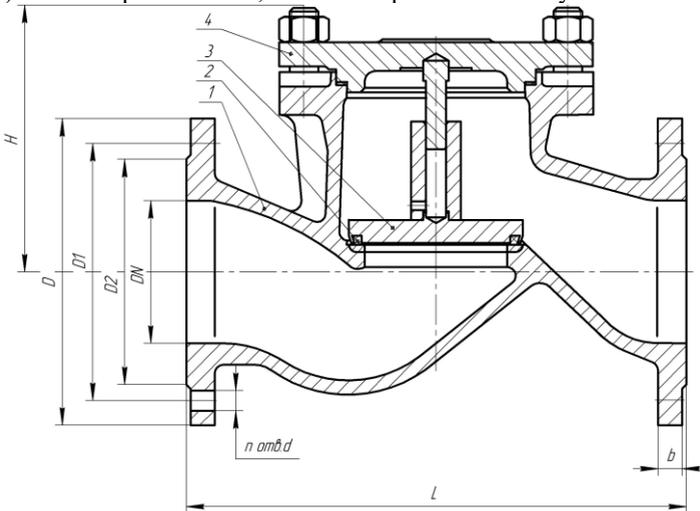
Конструкция обратного подъёмного клапана: 1 – корпус; 2 – уплотнительное кольцо; 3 – седло, 4 – крышка; 5 – крышка
